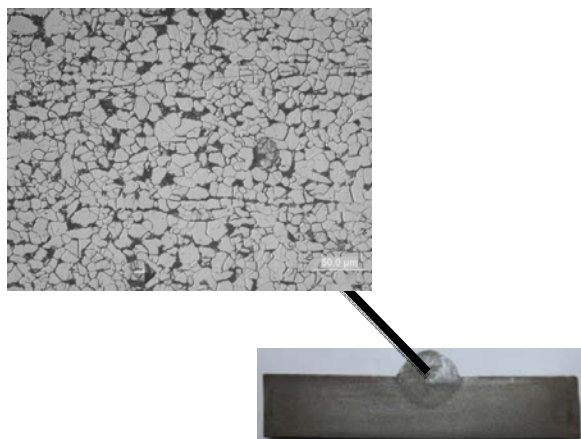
Структура сварного шва сварка в среде углекислого газа без применения модификаторов
